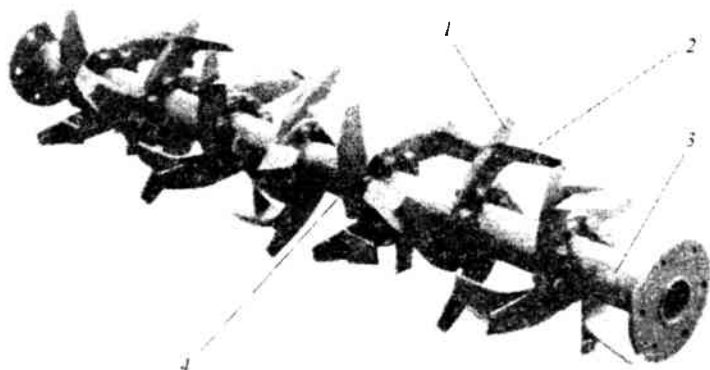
Ротационный рабочий орган с составными ножами для послойной обработки почвы: 1 – основной нож; 2 – дополнительный боковой Г-образный нож; 3 – вал барабана, 4 – диски
